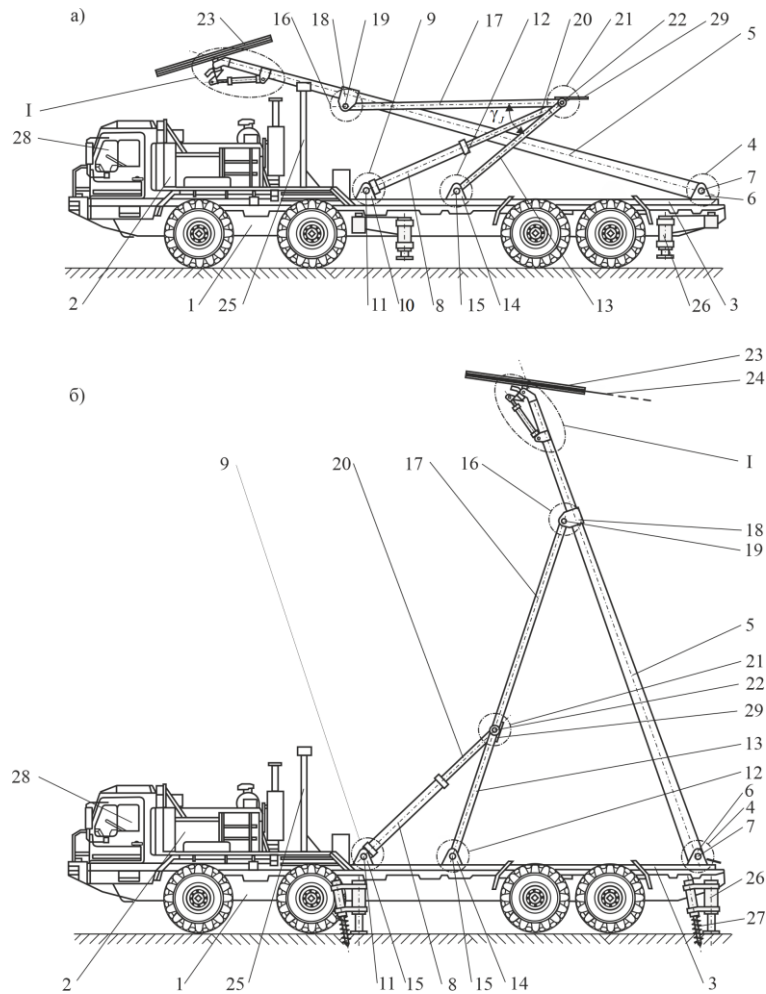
Общий вид сбоку базовой станции с концевым расположением концевой опоры и складывающейся штангой и обозначением основных конструктивных элементов:
